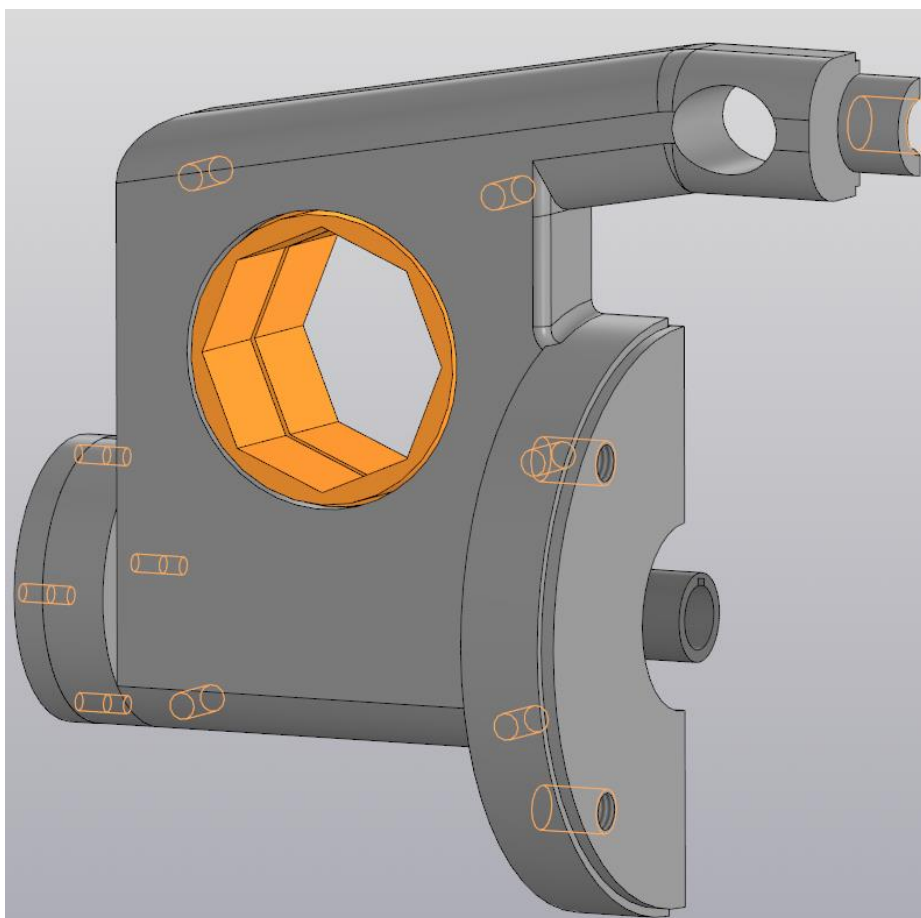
Сборка корпуса с червячной передачей и подшипниками
